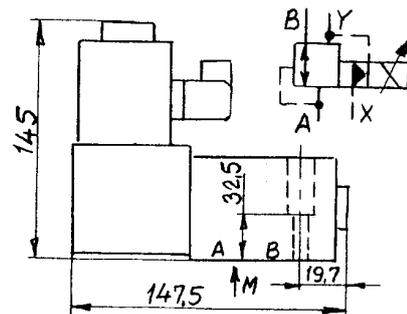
Клапаны VMY*10 Hydraulik-Ring
